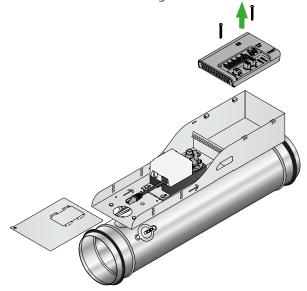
Nehmen Sie die Schläuche sowie die Kontakte von WISE CU ab. Schrauben Sie 2 Schrauben ab, die WISE CU festhalten (Schraube: PH1).
